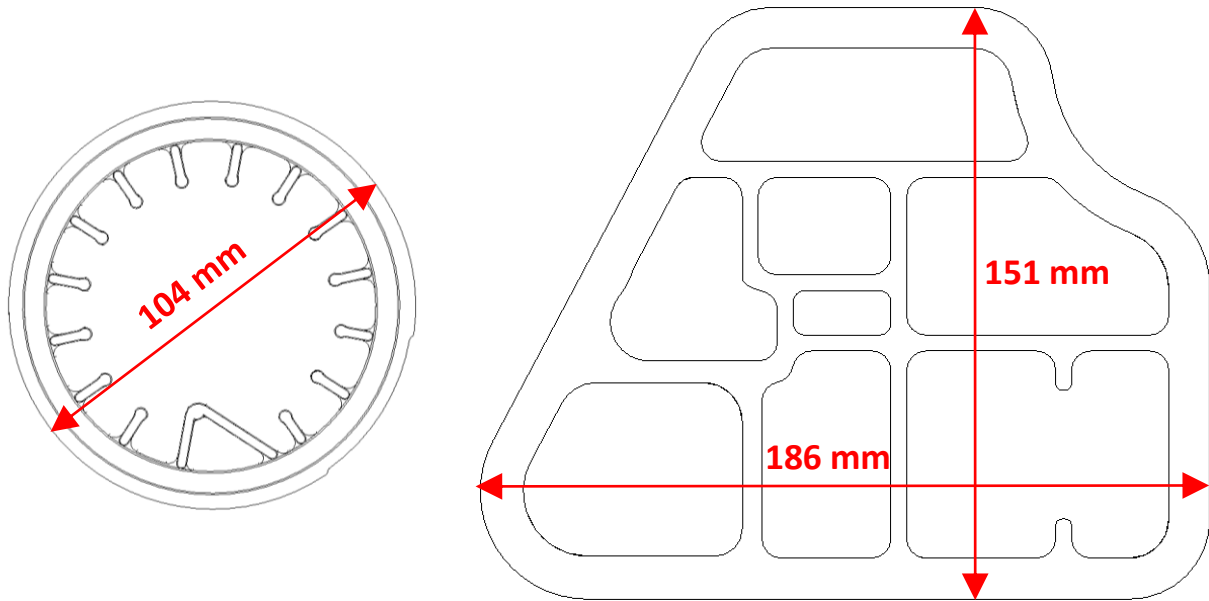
Dimensiones de las superficies de soldadura
